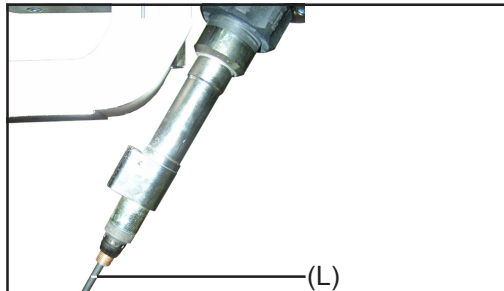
Drahtführungsseele Schweißbrenner ausbauen
